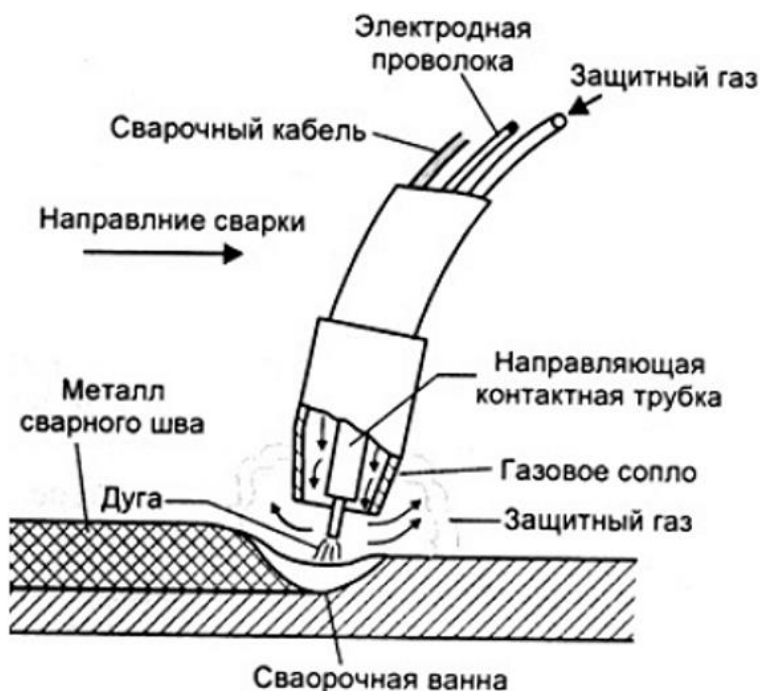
Сварки в среде углекислого газа
